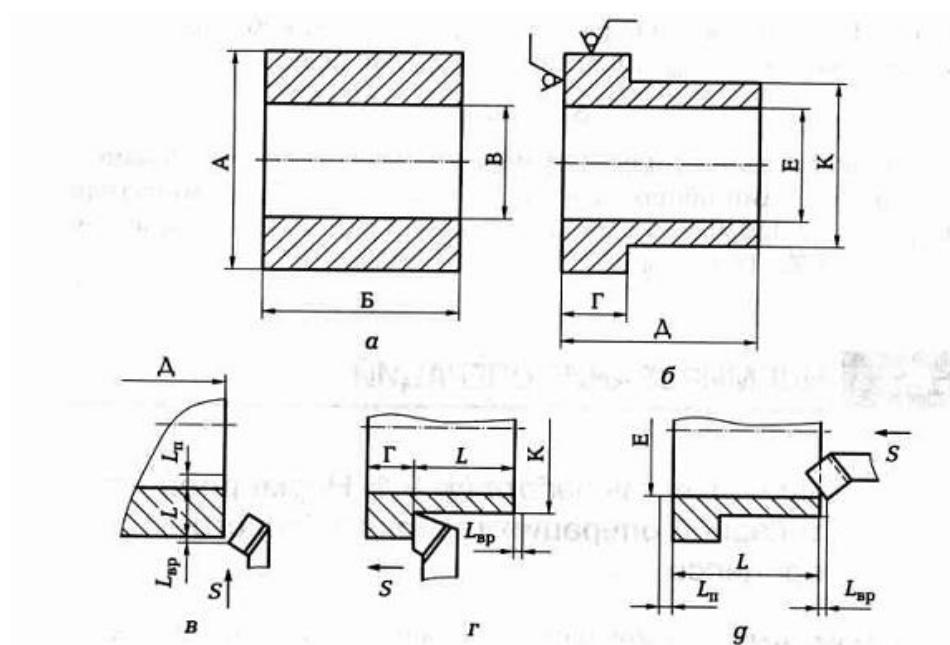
Обтачивание поверхностей: а – заготовка; б – обрабатываемая поверхность; в – подрезка торца; г – обтачивание до упора; д – растачивание поверхностей
